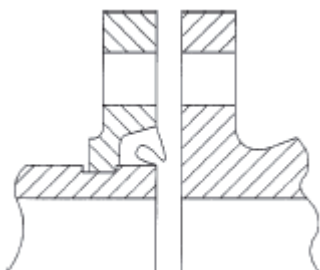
Modificando adaptadores de flange de 300 psig para aplicação de flange com face plana
